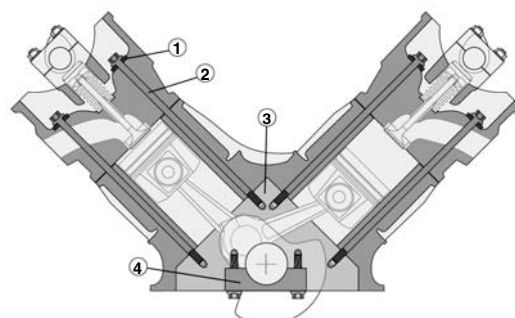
Болтовое соединение головки блока цилиндров прямо соединенные с опорой подшипников:
